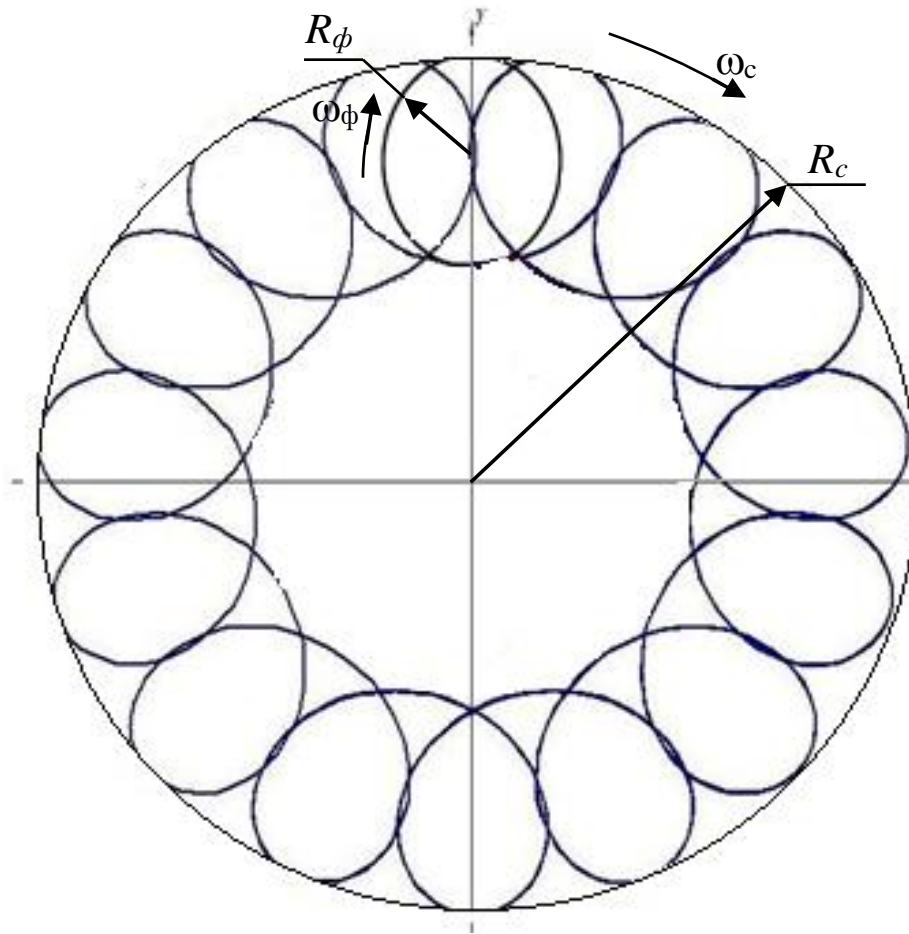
Траєкторія руху фрези при попутному фрезеруванні увігнутого контуру
